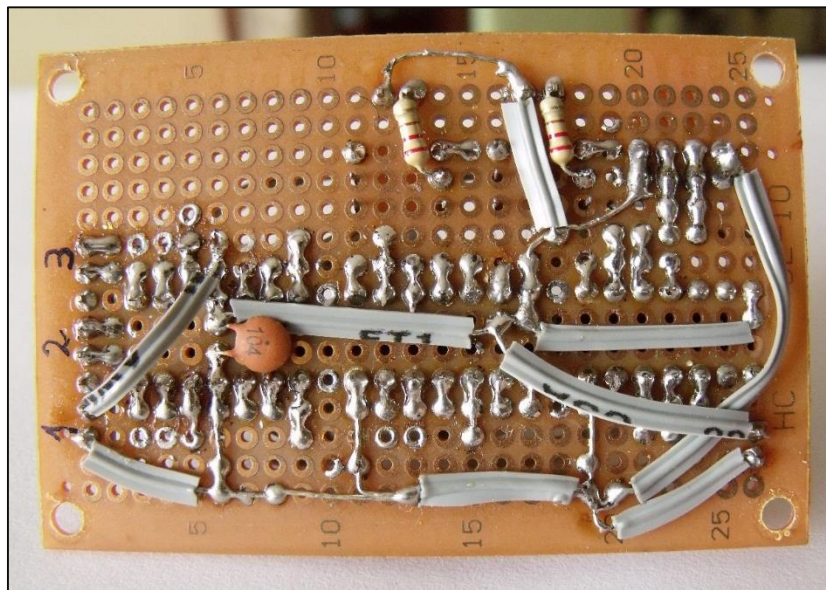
Proceso de soldado de la tarjeta de autobalance dinámico.
